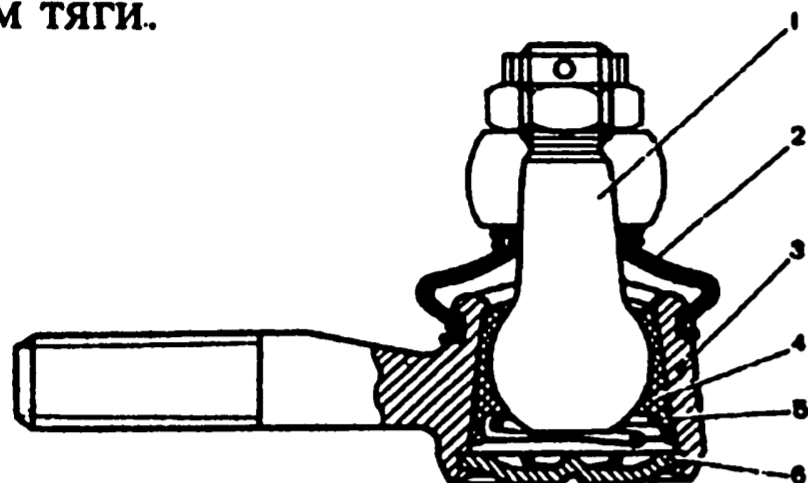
Разрез шарового шарнира тяги: 1 - шаровой палец; 2 - грязезащитный колпачок; 3 - корпус шарнира; 4 - вкладыш; 5 - пружина; 6 - заглушка
